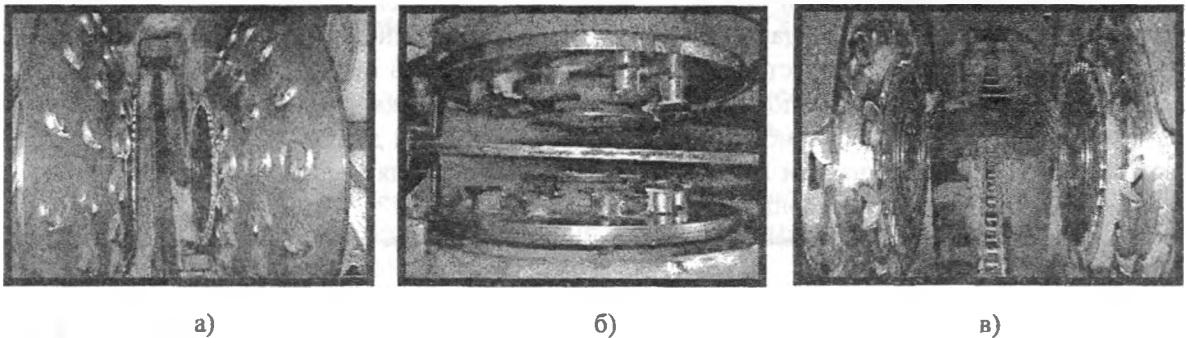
Режущий инструмент ФБС: а – фрезы фирмы SAB, б – фрезы конструкции БТИ, в – фрезы фирмы A.Costa righi
